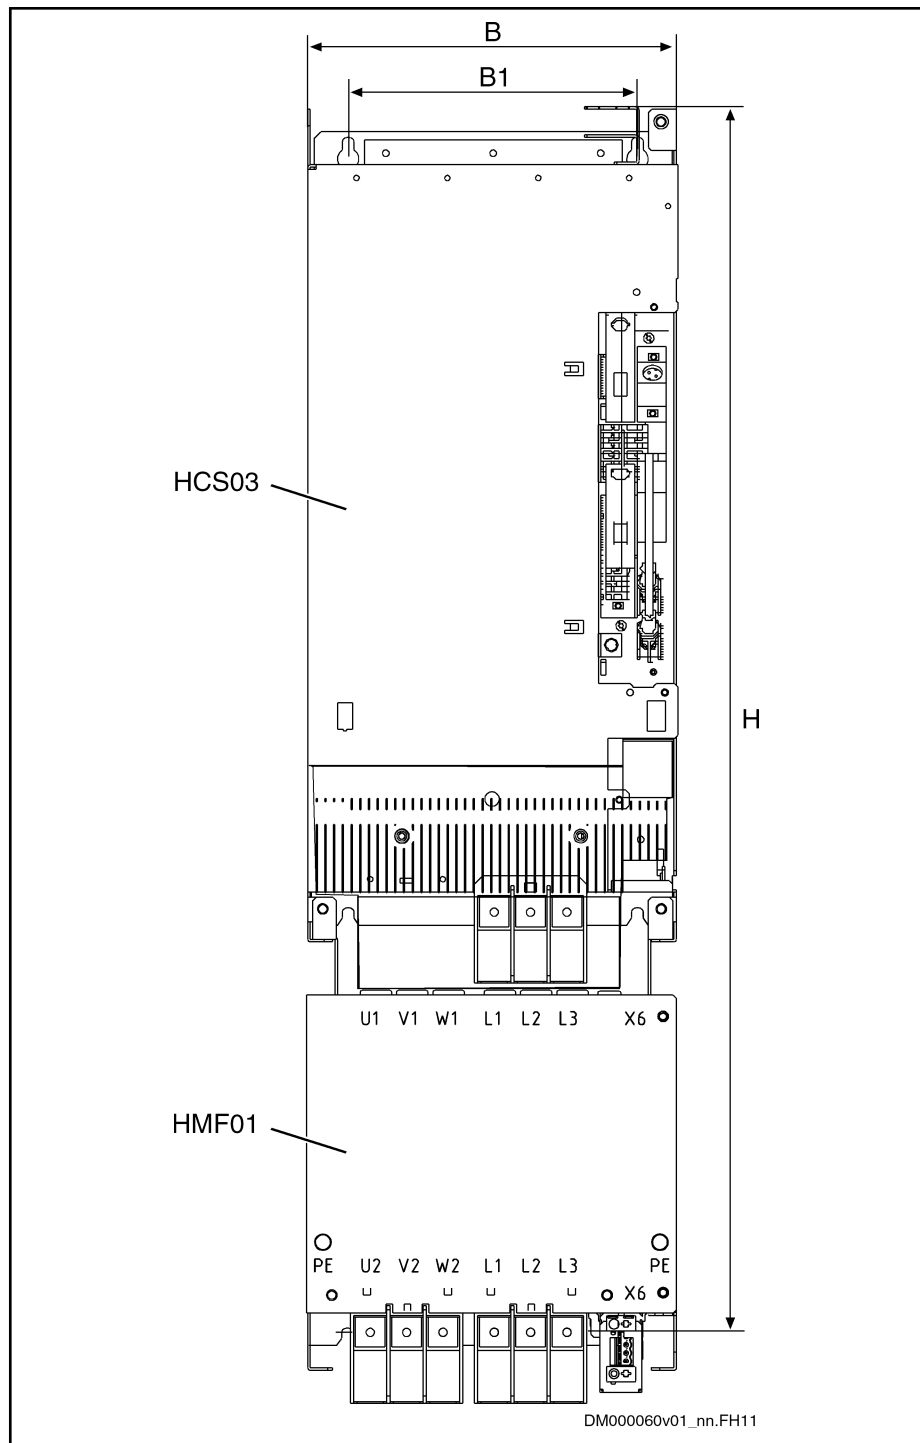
Montagebeispiel HCS03.1E-W0100, -0150, -0210 / Motorfilter HMF01
